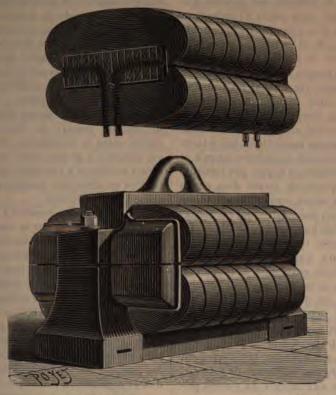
Vue d'ensemble et détails du transformateur Ferranti.
